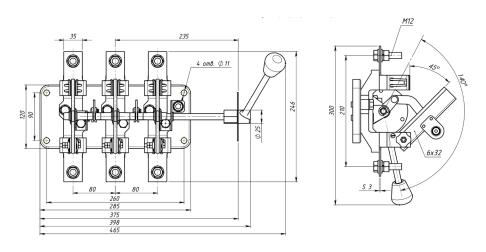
Разъединитель серии Р с боковой рукояткой РБ-6 на номинальный ток 630 A
